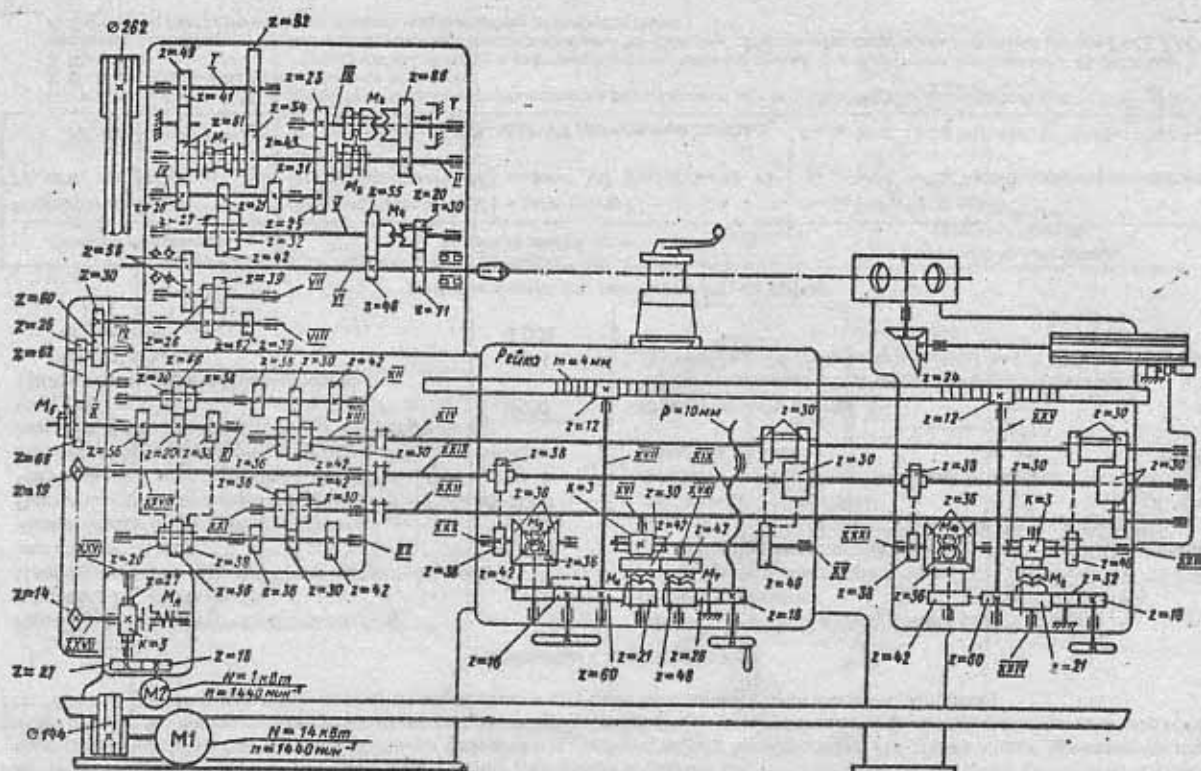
Кинематическая схема токарно-револьверного станка мод. 1П365
